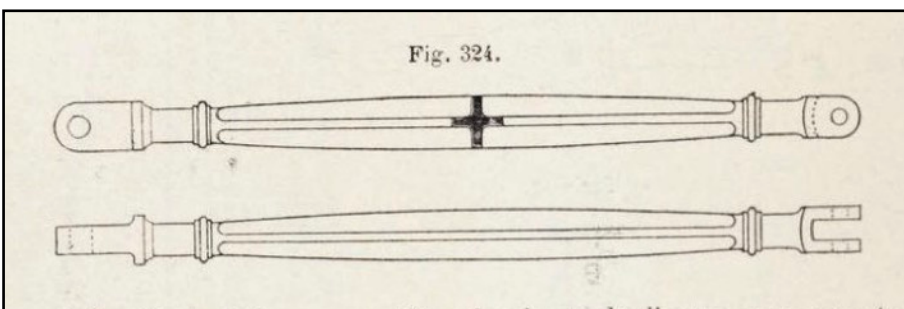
Plans d'une bielle possédant une tête simple et une tête bifurquée, Deschamps Henri, 1908.
